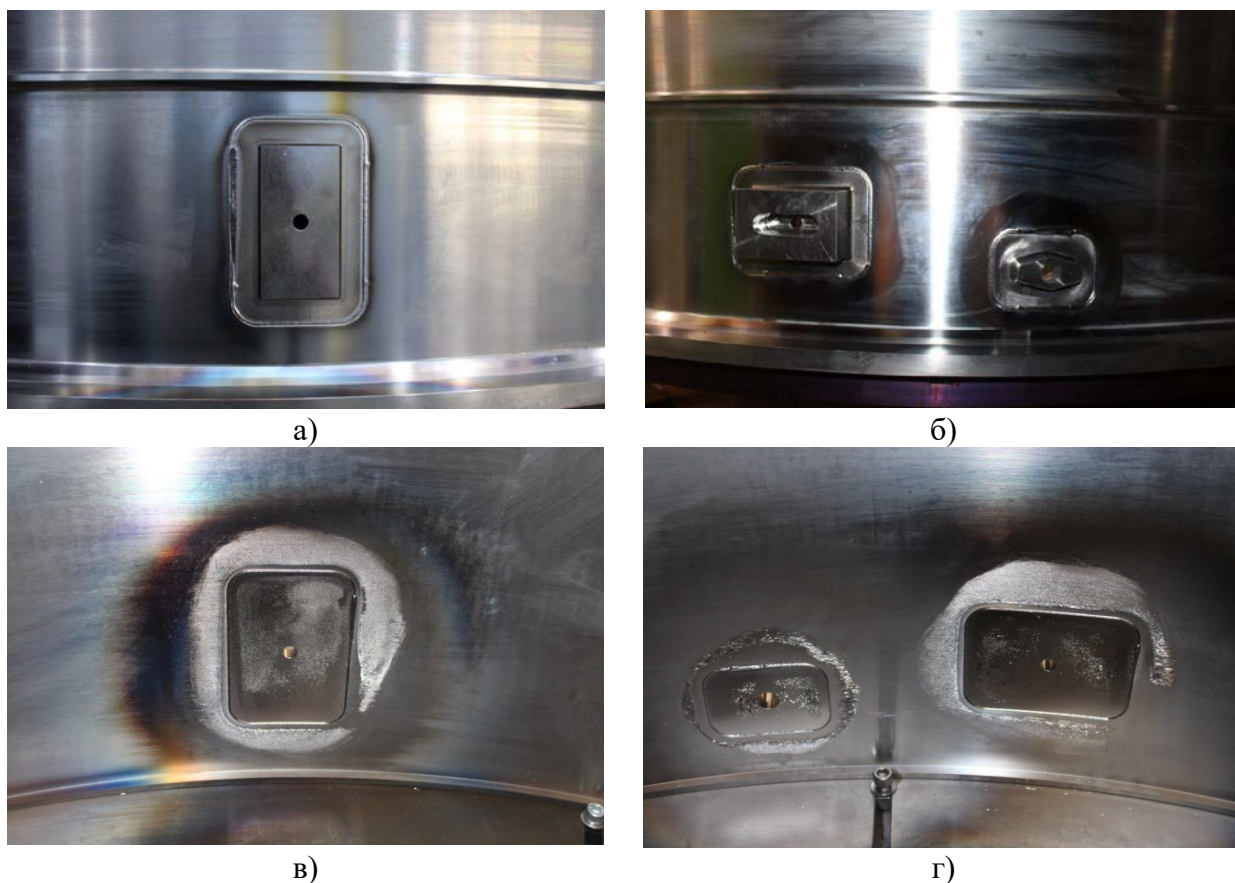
Внешний вид сварных швов сваренных ЭЛС:
